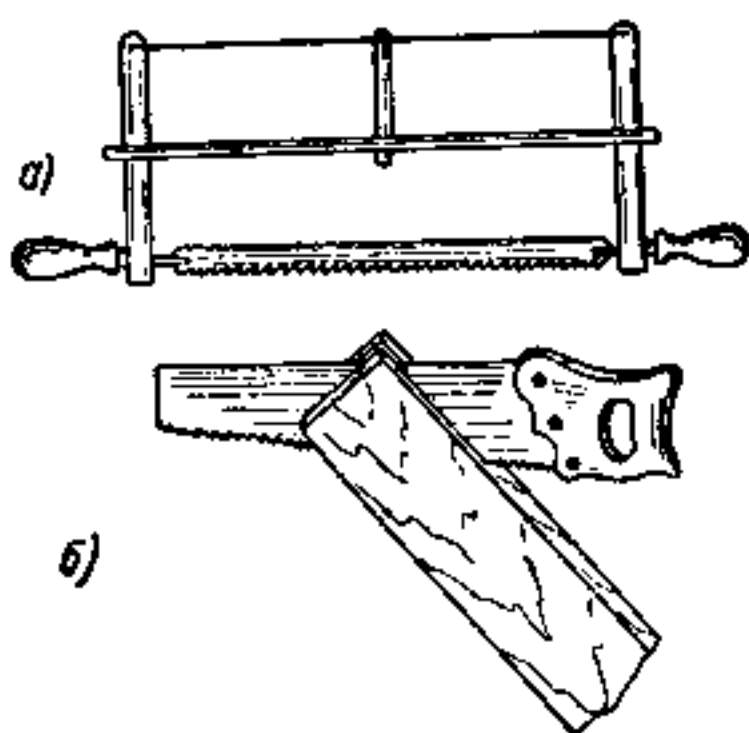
Пилы: а) — лучковая, б) — ножовка
